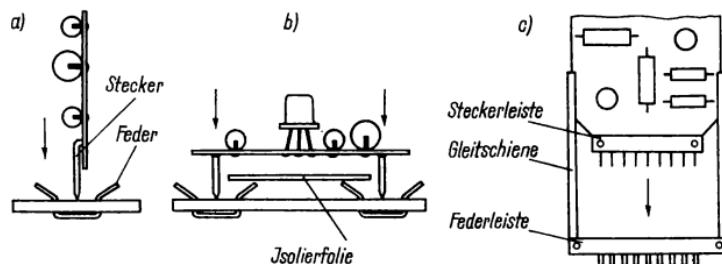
Amateurlösungen für Baugruppenanschlüsse
